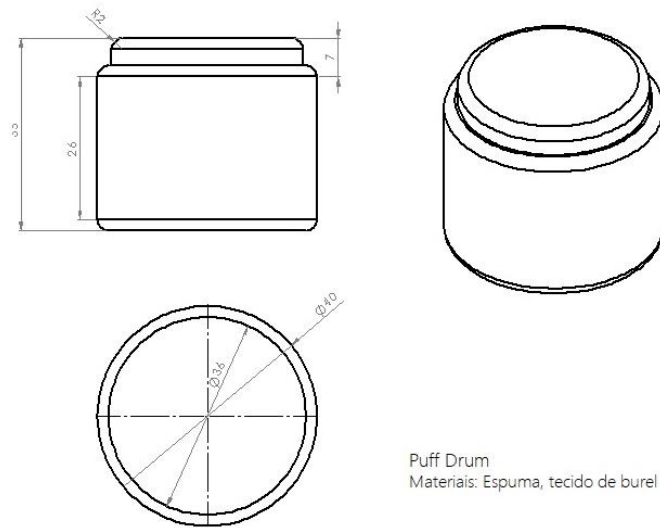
Desenho técnico CAD 3D do conceito Drum Burel (Fonte: Autor)
